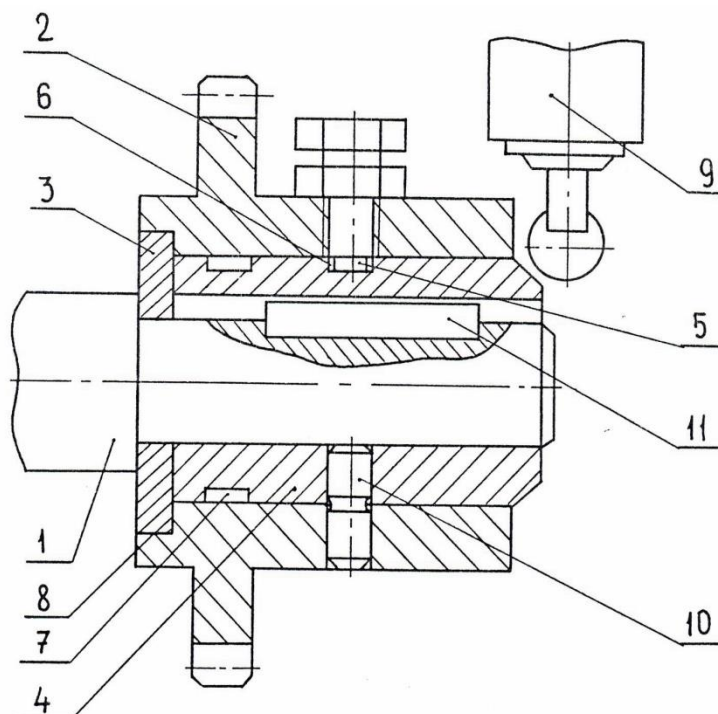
Устройство для аварийного выключения привода МПК:
